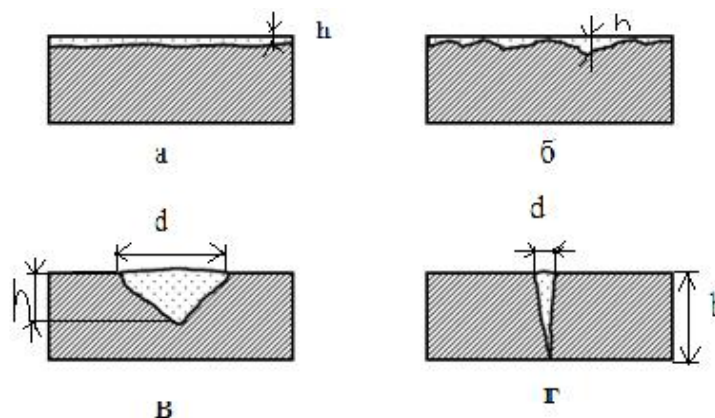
Основные типы коррозионного износа натуральных культиваторных лап (а – сплошной равномерный; б – сплошной неравномерный; в – язвенный; г – точечный. Обозначения: h – глубина; d – ширина; b – толщина изделия
